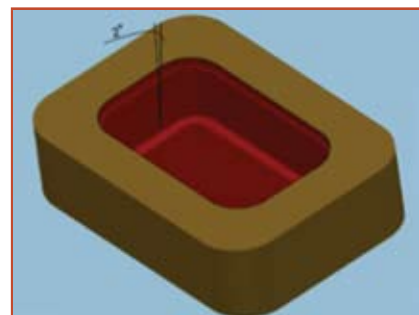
Эскиз пресс-формы для упаковки, обработанной методом контурного шлифования на станке *RXP 500DS
